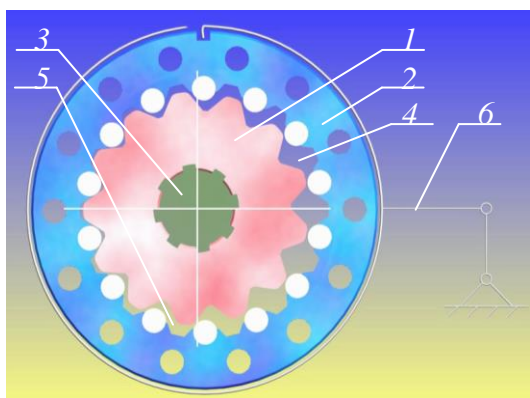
Компенсирование планетарного движения вытеснителей с помощью внешнего компенсирующего механизма: 1 – охватываемый вытеснитель; 2 – охватывающий вытеснитель; 3 – вал приводного устройства; 4 – зона нагнетания; 5 – зона слива; 6 – двухзвенный рычаг
